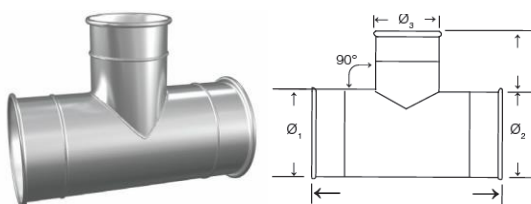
Tê QFS (QFS Oil Mist & Cutting Fluid)
